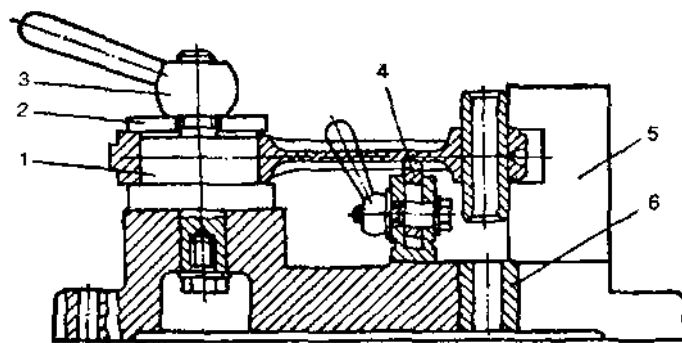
Приспособление для контроля и рихтовки шатунов:
